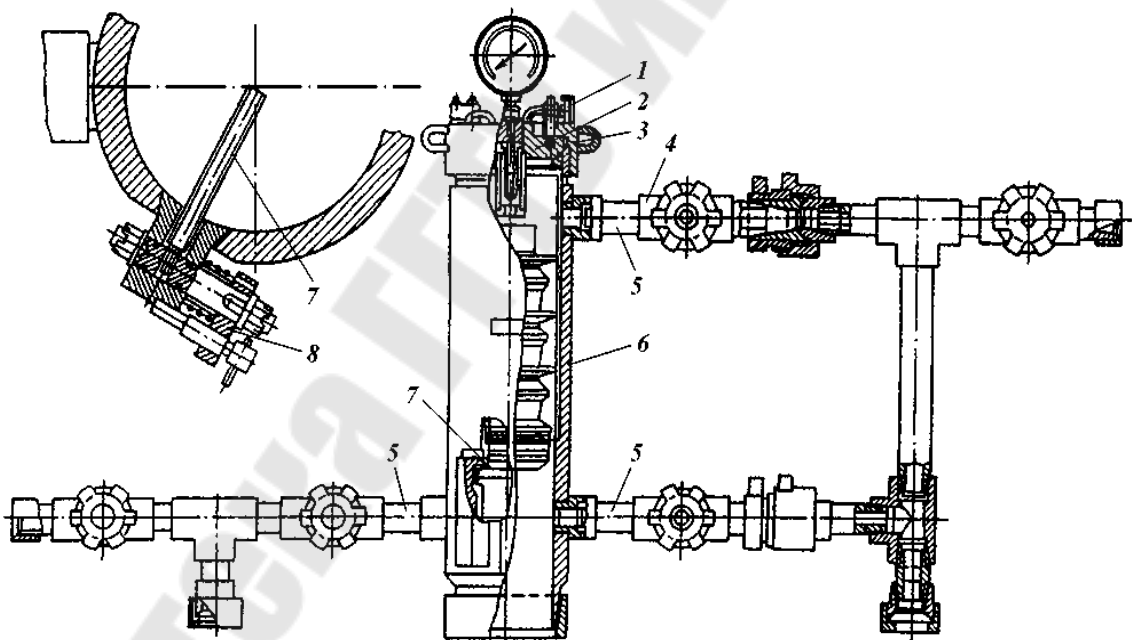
Универсальная цементировочная головка типа ГЦУ: 1 – съемник; 2 – крышка; 3 – гайка; 4 – проходной кран; 5 – соединительные линии; 6 – корпус; 7 – фиксатор пробки; 8 – указатель (сигнализатор) начала движения пробки
